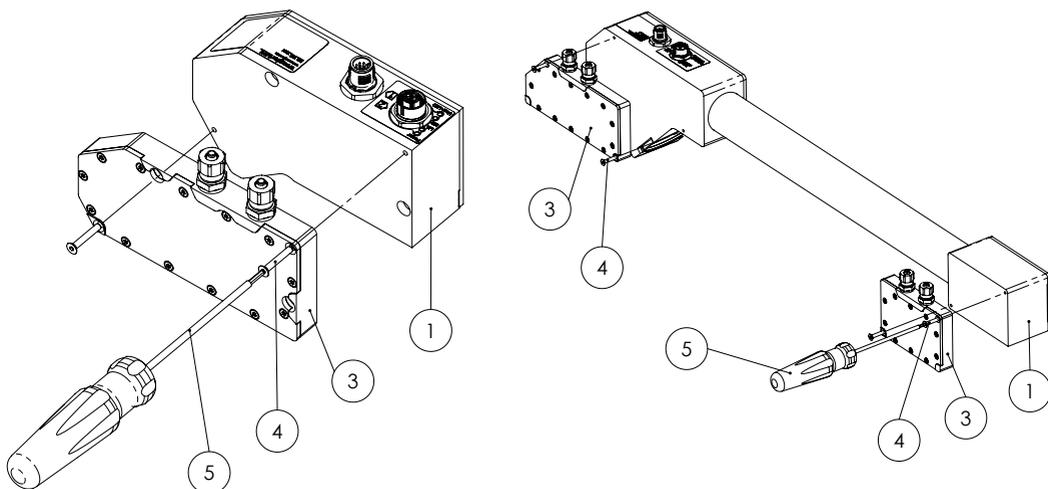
Montage Kühlmodul bei weCat3D MLWLxxx
